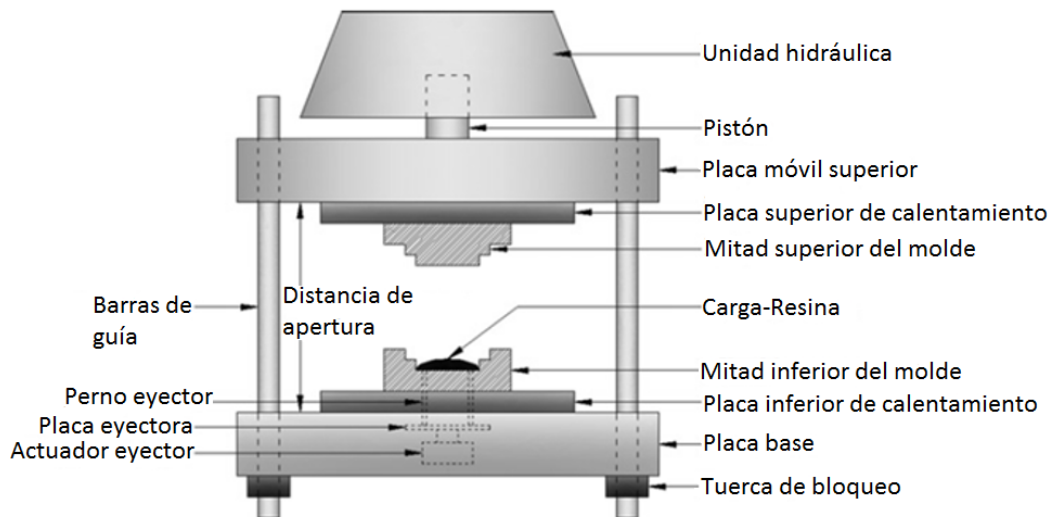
5 Prensa utilizada durante el moldeo por compresión en caliente [55]
